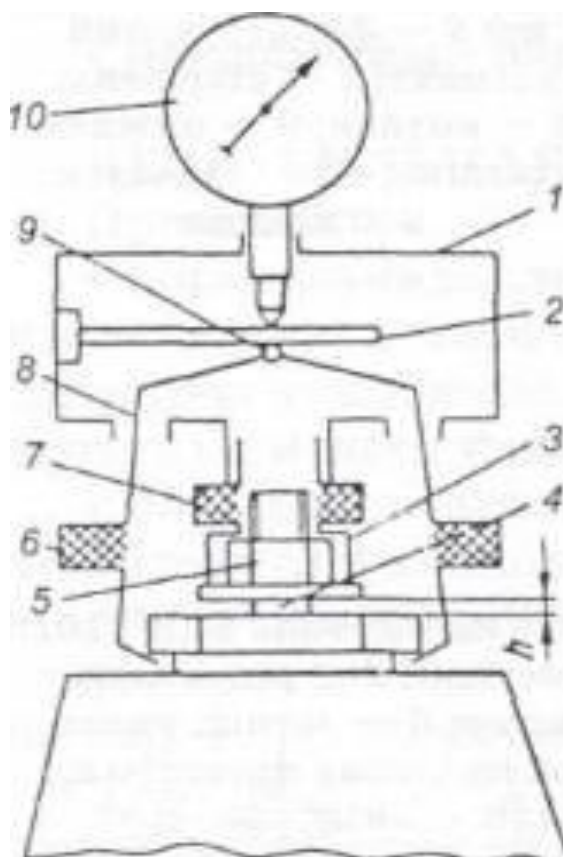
Приспособление КИ-9912 для проверки степени загрязнения центрифуги:
